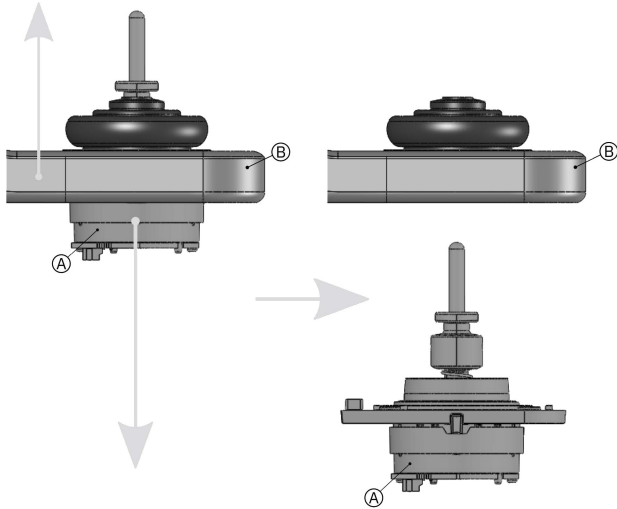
Entfernen der Joystick-Baugruppe samt Manschette aus dem Chassis
